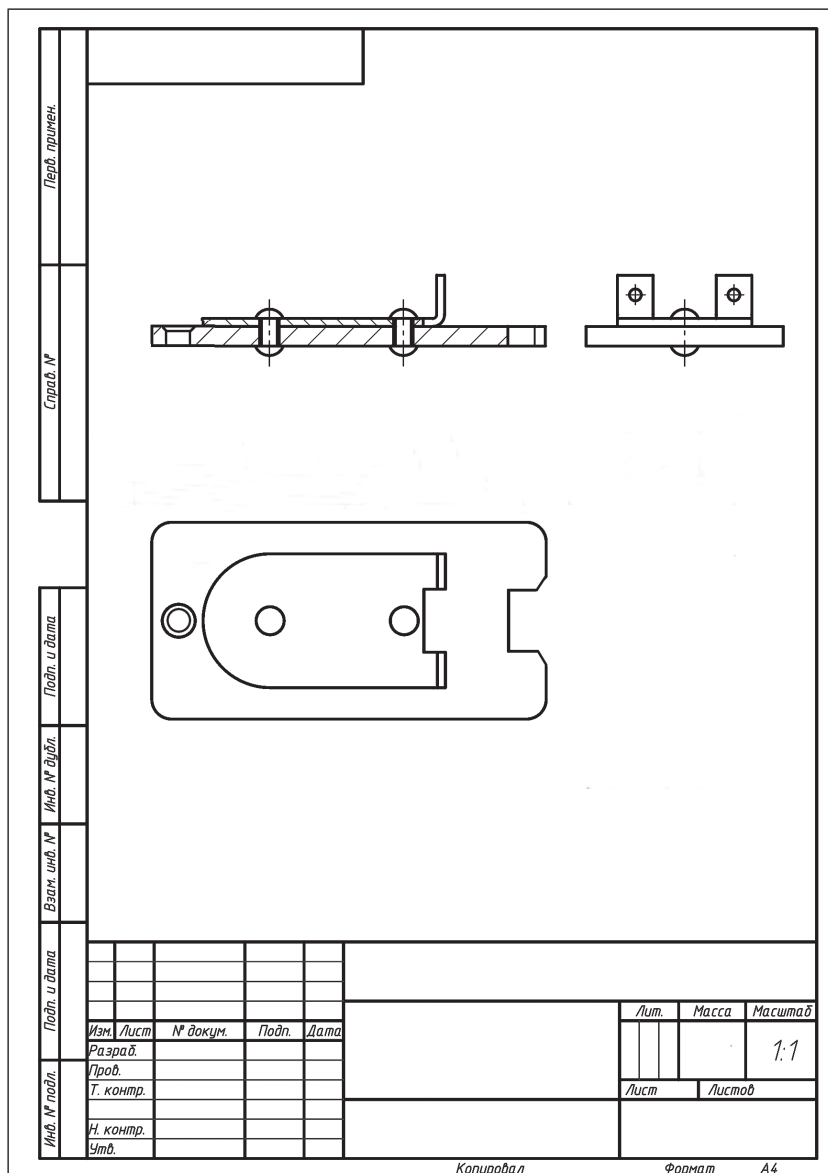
Доработка изображений 2D-видов для сборочного чертежа изделия «Кронштейн»
